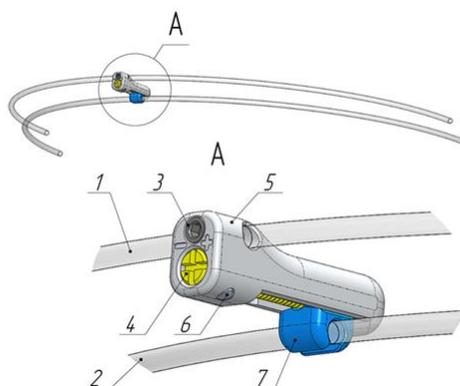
А – регулирующий механизм, 1,2-пластиковые шины, 3-установочный винт, 4-регулирующий винт, 6-штифт, 7-серьга
